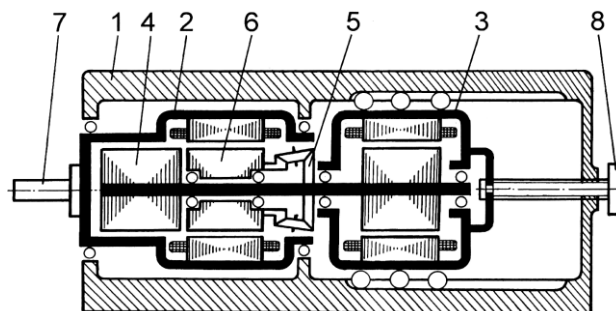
Компаундный асинхронный биротативный каскад (1-корпус привода; 2-биротативный двигатель; 3-дополнительный двигатель; 4-ротор противовключения; 5-конический редуктор; 6-генераторный ротор; 7-выходной вал; 8-регулирующий винт)
